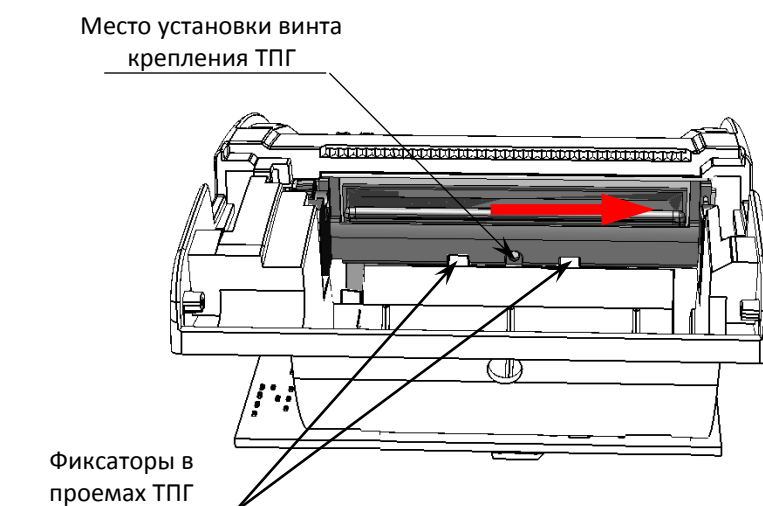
Установка ТПГ в нижнюю часть корпуса ККТ
